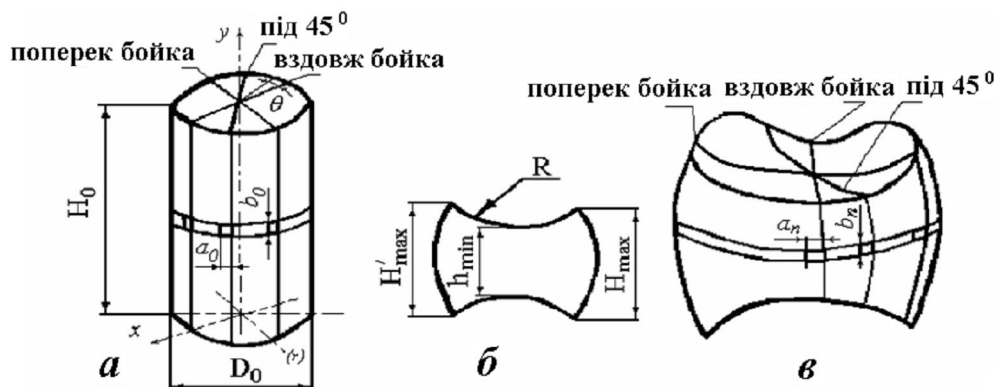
Схема осаджування циліндричної заготовки випуклими бойками
